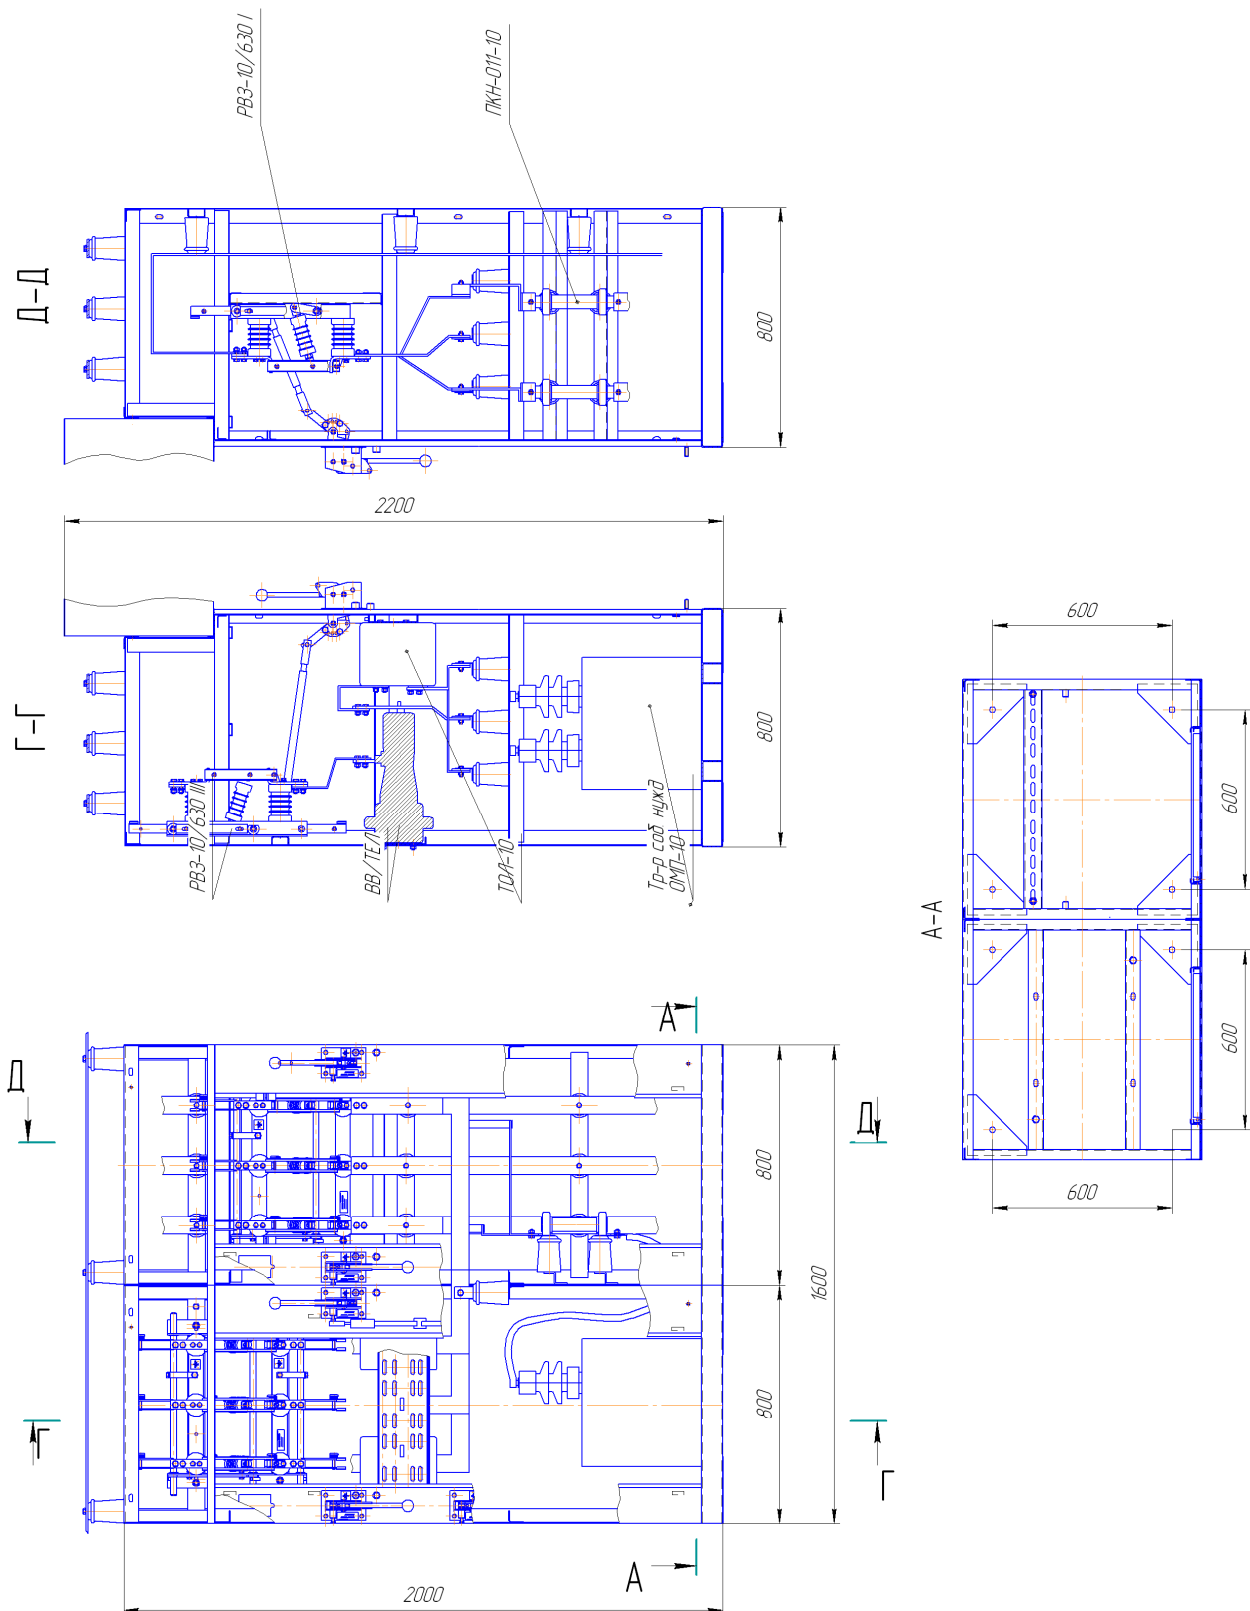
Габаритные и установочные размеры ячейки КСО-393М-12В
